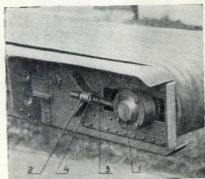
Механизм натяжения ленты транспортёра: 1 — гнездо подшипника; 2 — втулка упорная; 3 — винт натяжной; 4 — контргайка.
